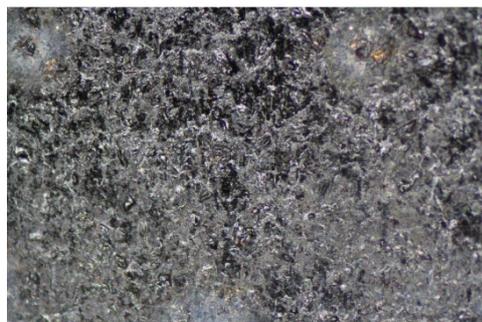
Исходное состояние сварного шва после зачистки
